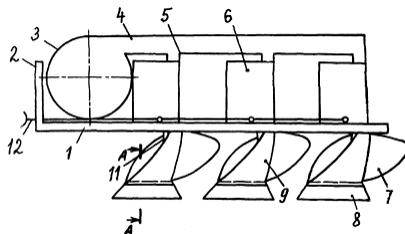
Схема плуга-удобрителя (вид сбоку)
